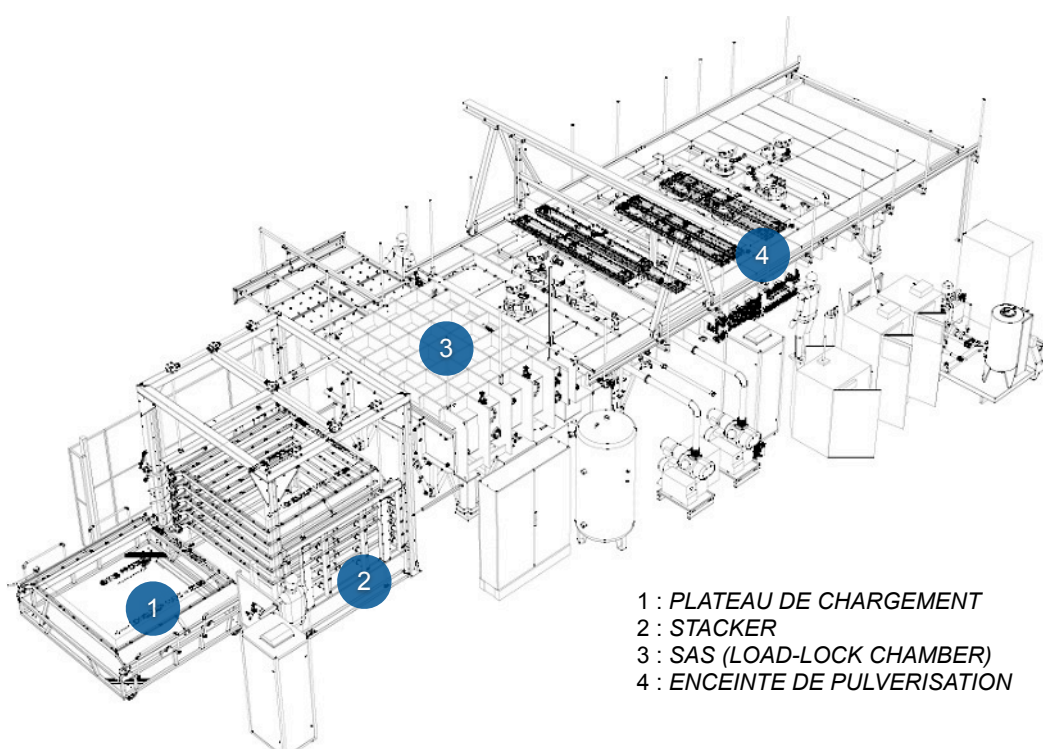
Vue 3D de la machine PACA2M.
